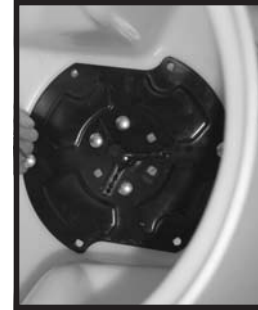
Pièces requises pour l'assemblage du tambour.
